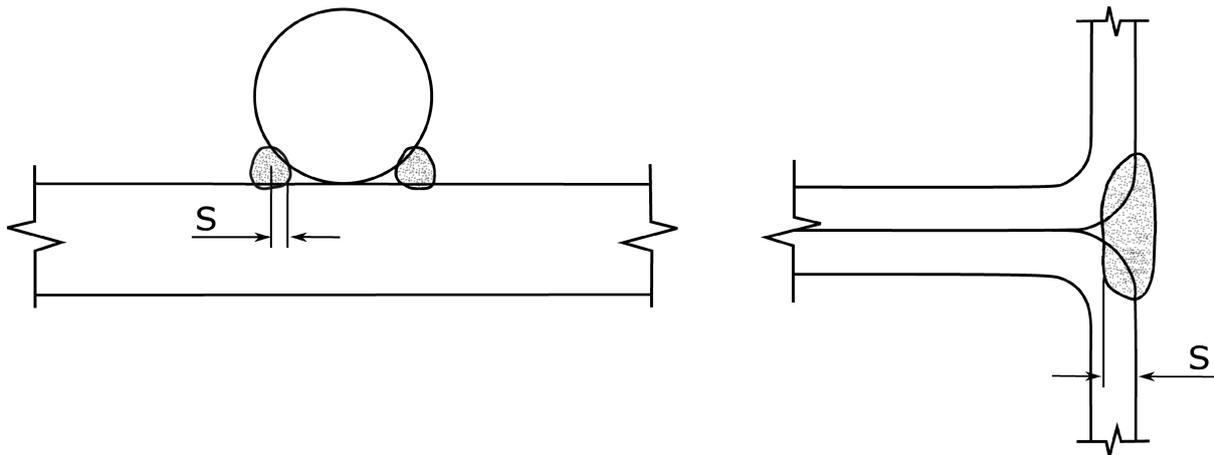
Eindringtiefe „s“ für Bördelnähte
